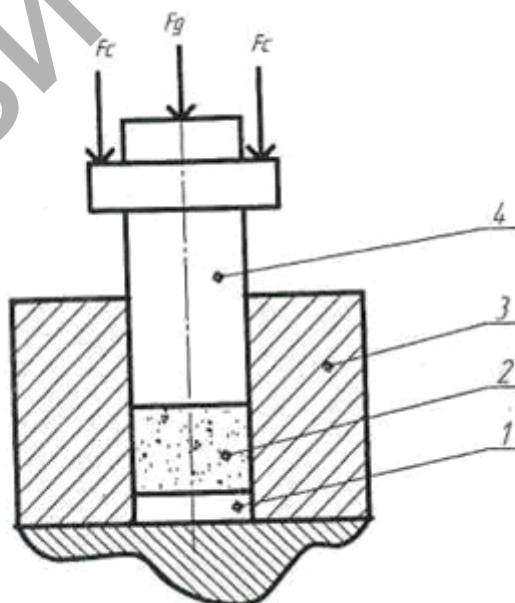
Схемы совместного наложения статической и динамической нагрузок при прессовании порошков
